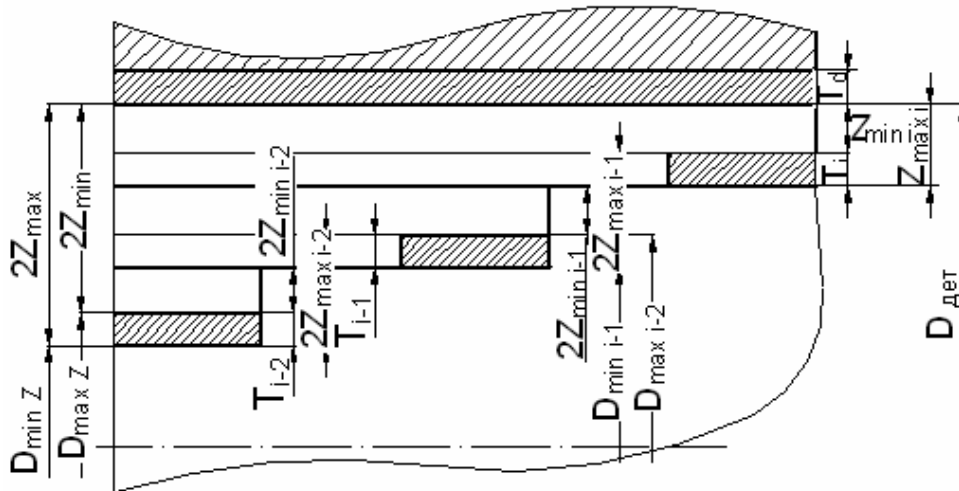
Схема зв'язків міжперехідних розмірів, припусків і допусків для охоплюваних поверхонь
